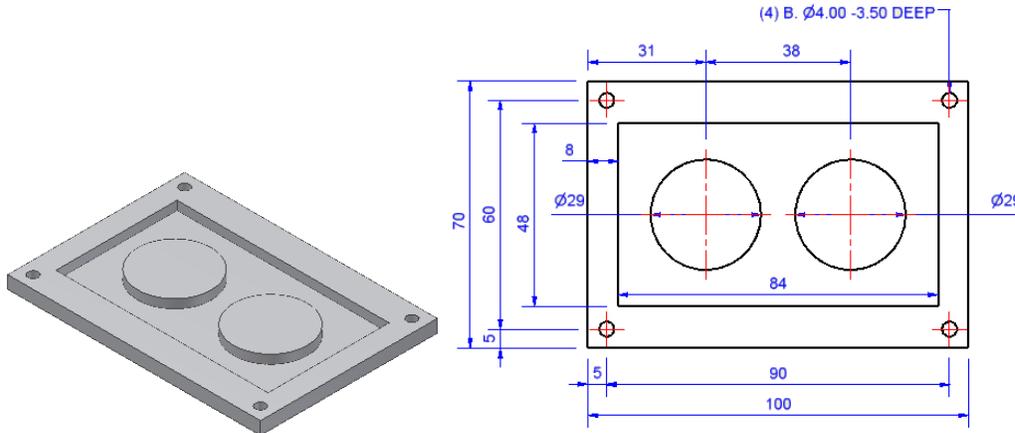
Vista isométrica de la pieza a maquinar. Figura 16. Vista superior de la pieza a maquinar
